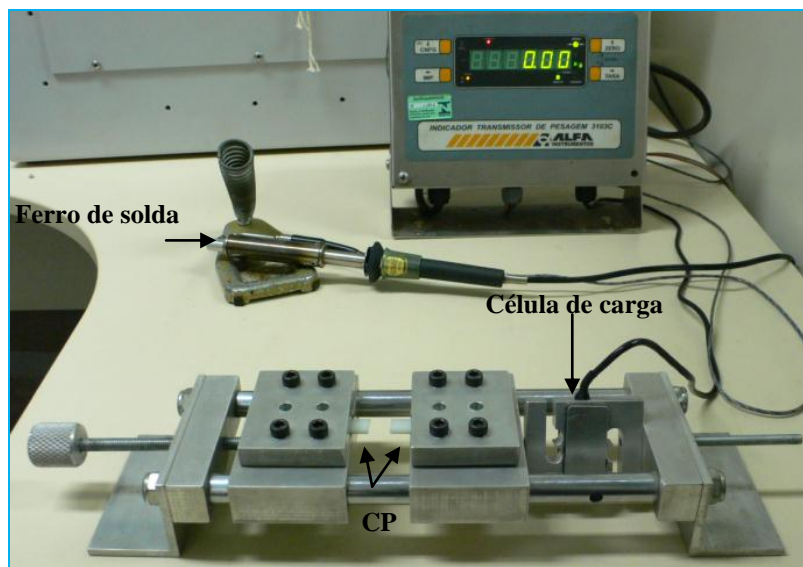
Equipamento de solda pelo método de aquecimento por placas.
